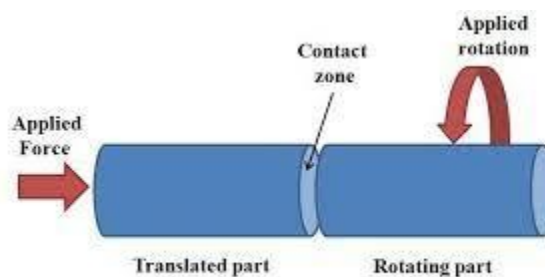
Différents étapes de soudage par friction [22]
